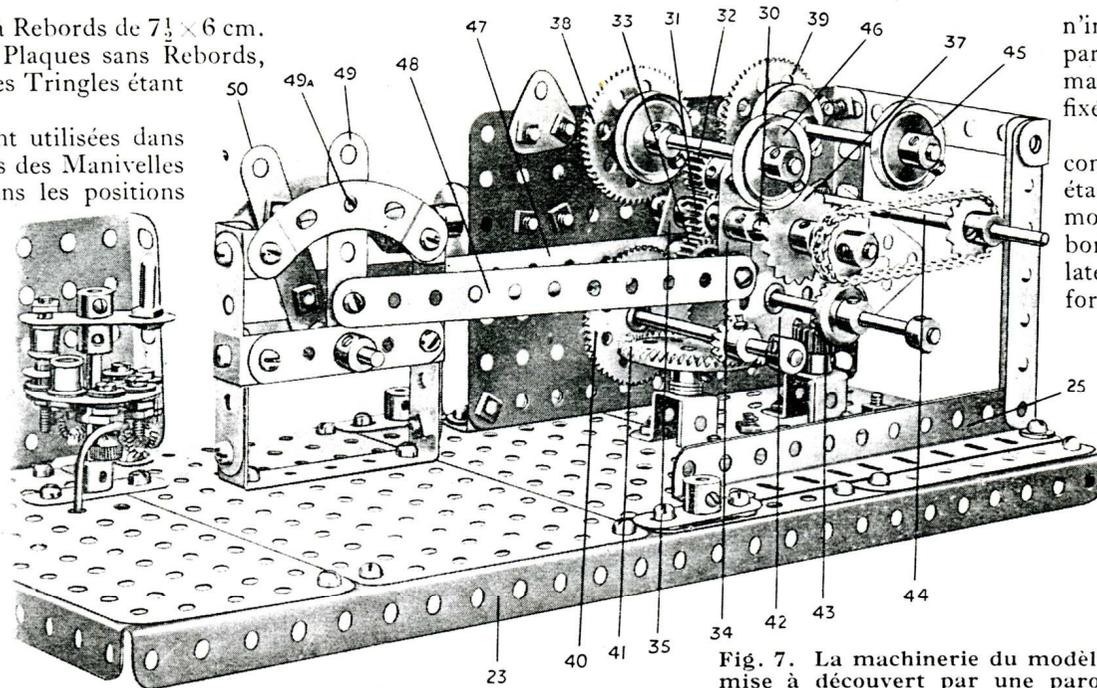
La machinerie du modèle mise à découvert par une paroi enlevée
